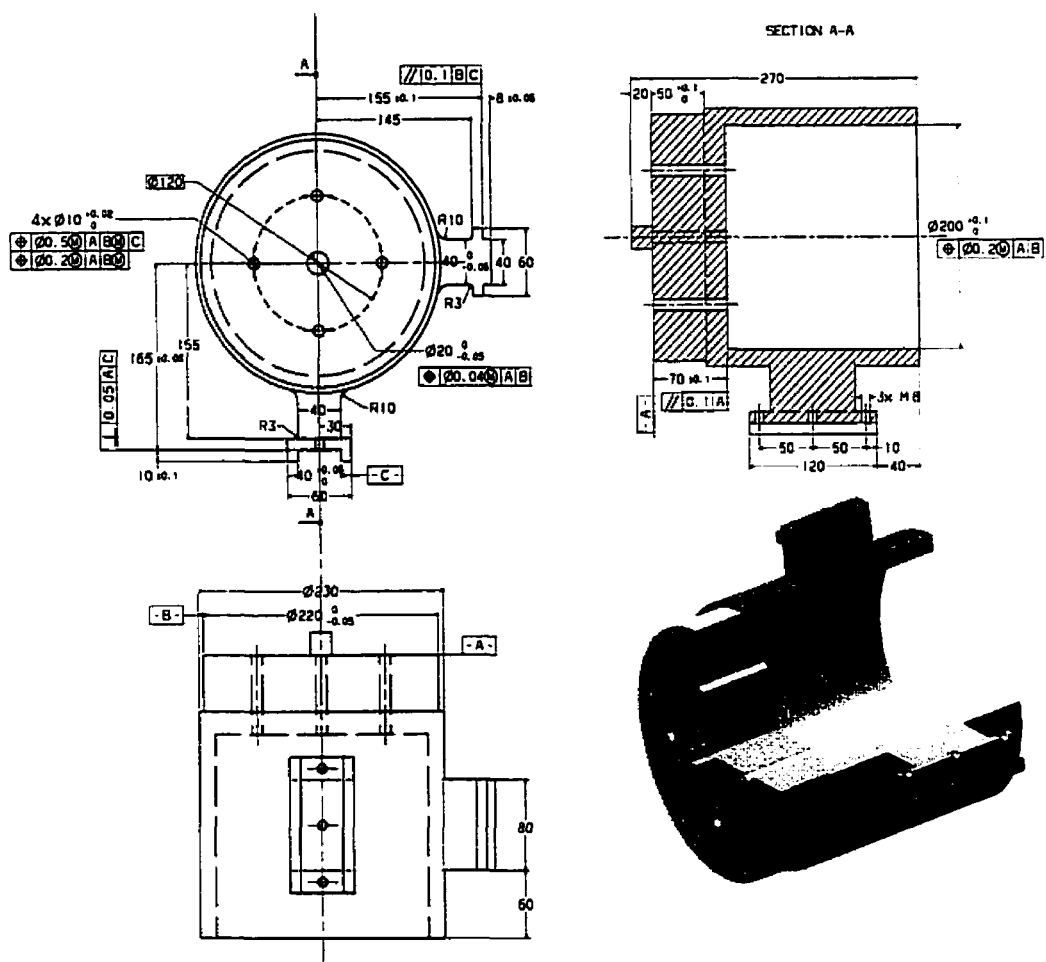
Vue isométrique et dessins de définition (ex. 1)
